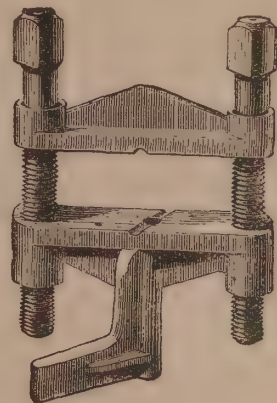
stellt Le Count's neue Stahlklammer dar, welche sehr stark und gut gemacht ist. Die Schraube ist flachgängig und mit einem Kugelenknopf an ihrem Ende versehen, welcher sich von selbst jeder Unregelmässigkeit anpasst, ohne die Schraube zu verbiegen.
